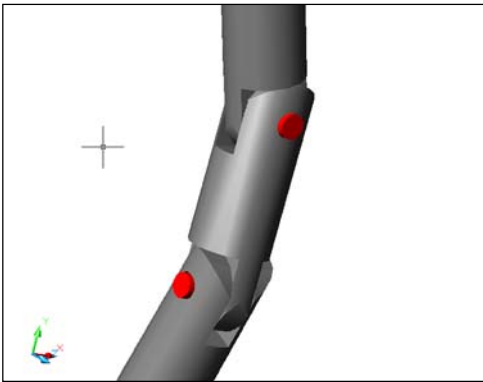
Detalle del sistema cardano, planteado como solución al problema del accionamiento a distancia de las válvulas bajo cubierta.
